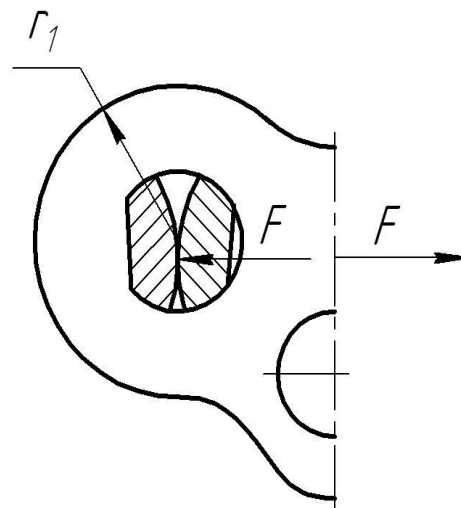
Пластина зубчатой цепи повышенной несущей способности
